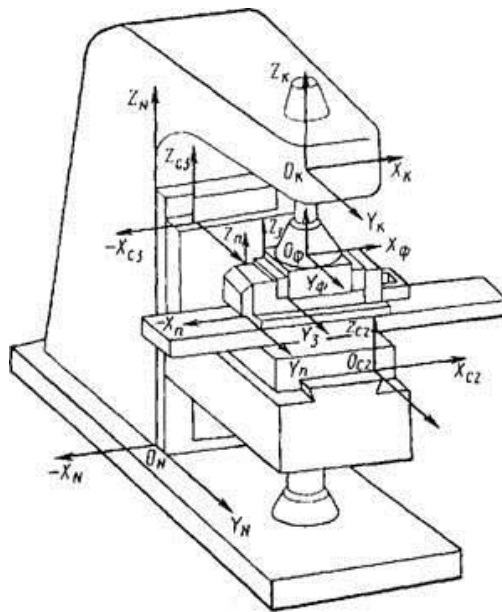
Траектории главного и вспомогательных движений вертикально-фрезерного станка 6P12
